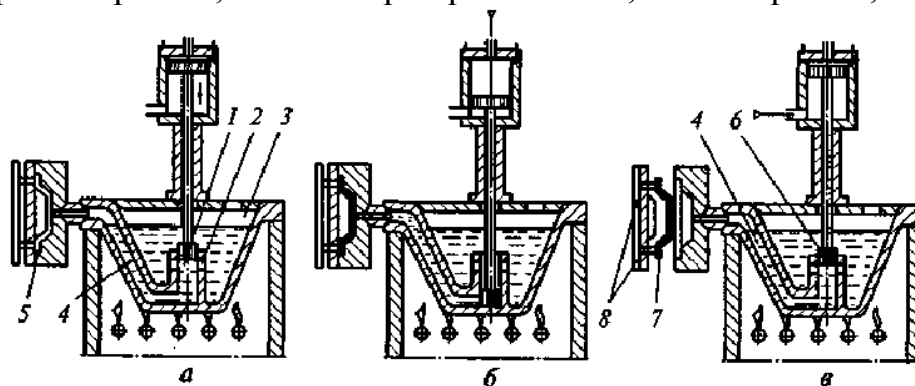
Схема технологического процесса литья под давлением на машине с горячей камерой прессования: *а* — заполнение камеры прессования расплавом; *б* — запрессовка; *в* — раскрытие пресс-формы и выталкивание отливки; 1 — камера прессования; 2 — заливочное отверстие; 3 — тигель с расплавом; 4 — обогреваемый канал; 5 — пресс-форма; 6 — пресс-поршень; 7 — отливка; 8 — толкатели
